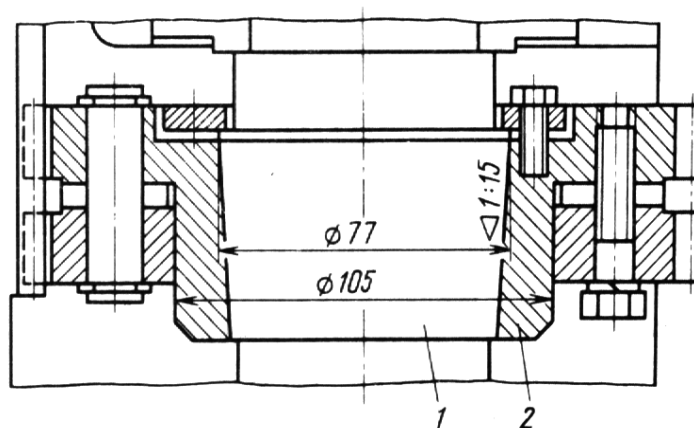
Установка розрізних зубчастих коліс на конусний вал
